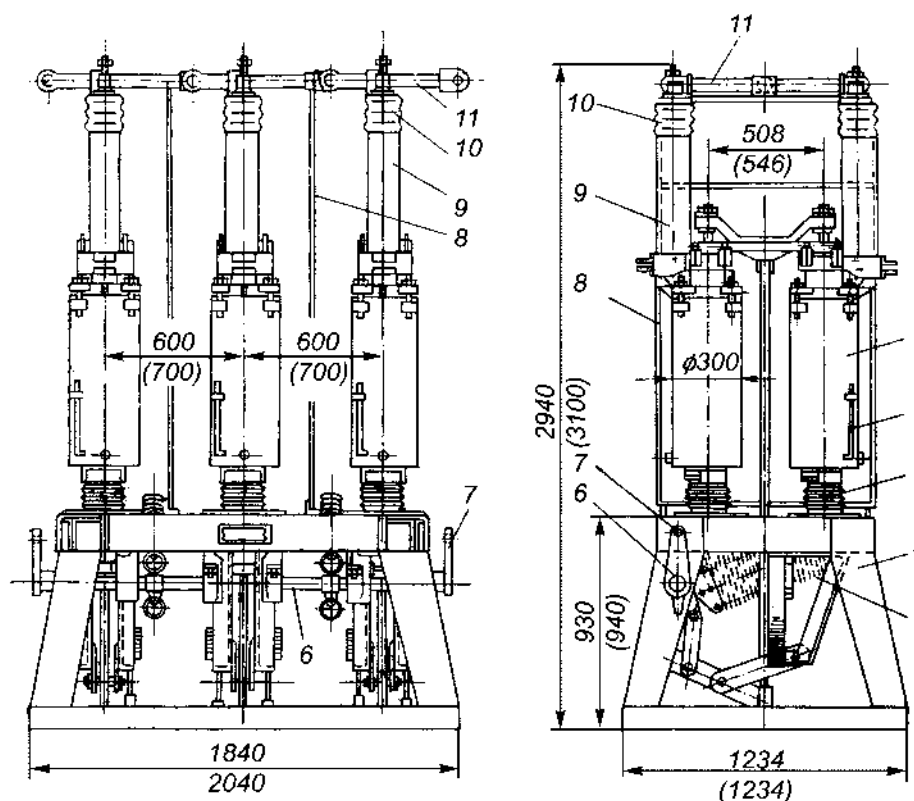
Общий вид выключателя типа МГ-10 и МГ-20 (в скобках даны размеры выключателя МГ-20): 1 – бачок; 2 – маслоуказательная трубка; 3 – опорный изолятор; 4 – опорная стальная рама; 5 – отключающая пружина; 6 – приводной вал; 7 – приводной рычаг; 8 – съёмная изоляционная перегородка; 9 – маслоотделитель; 10 – изоляционная фарфоровая трубка; 11 – газоотводящая трубка
